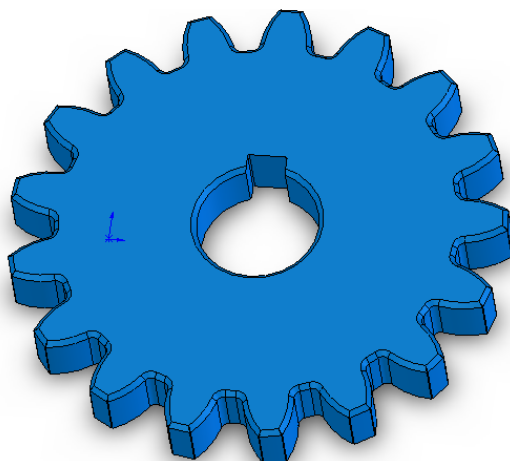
Объемная твердотельная модель цилиндрического зубчатого колеса.
